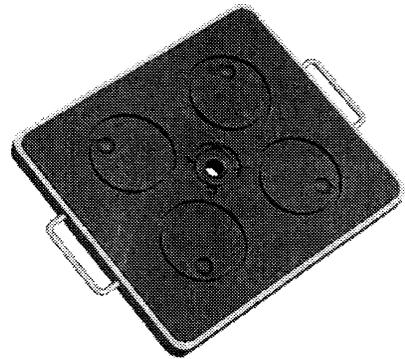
Песчано-глинистая форма для сборки вертикальной стопки (17 шт. в стопке)
